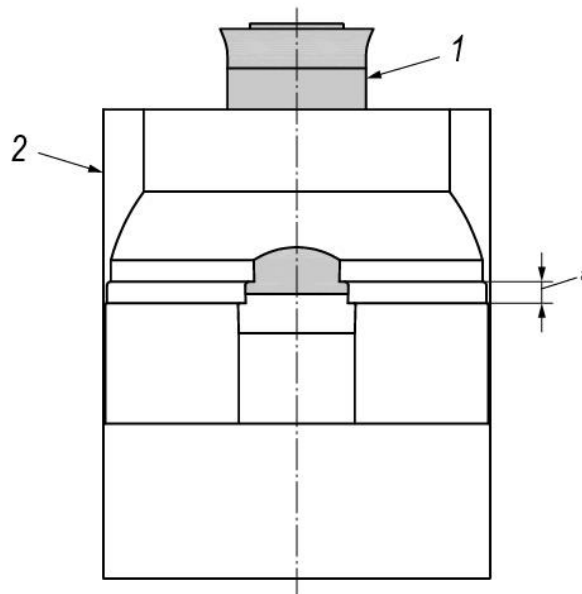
Эталонный гнездовой соединитель для испытания конуса соединителя
